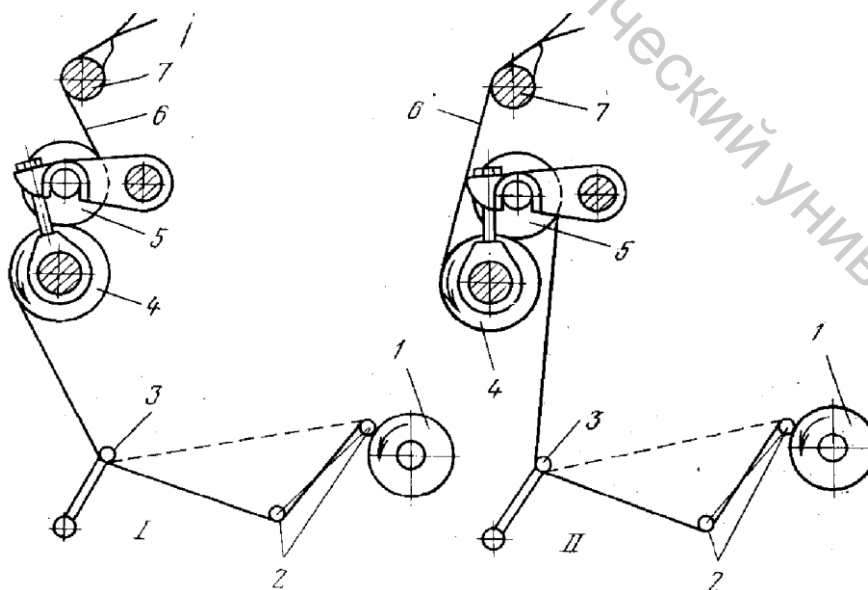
Схема движения товара в товарном регуляторе
